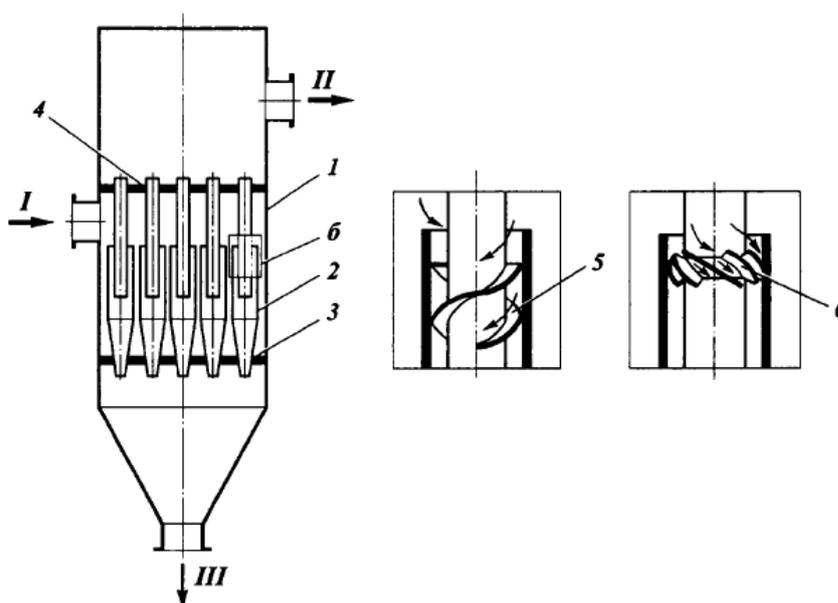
Конструкция батарейного циклона: а — продольный разрез; б — конструкции закручивающих устройств; 1 - корпус; 2 - циклонные элементы; 3, 4 - трубные решетки; 5 – винтовая лента; 6 - лопастная розетка.
